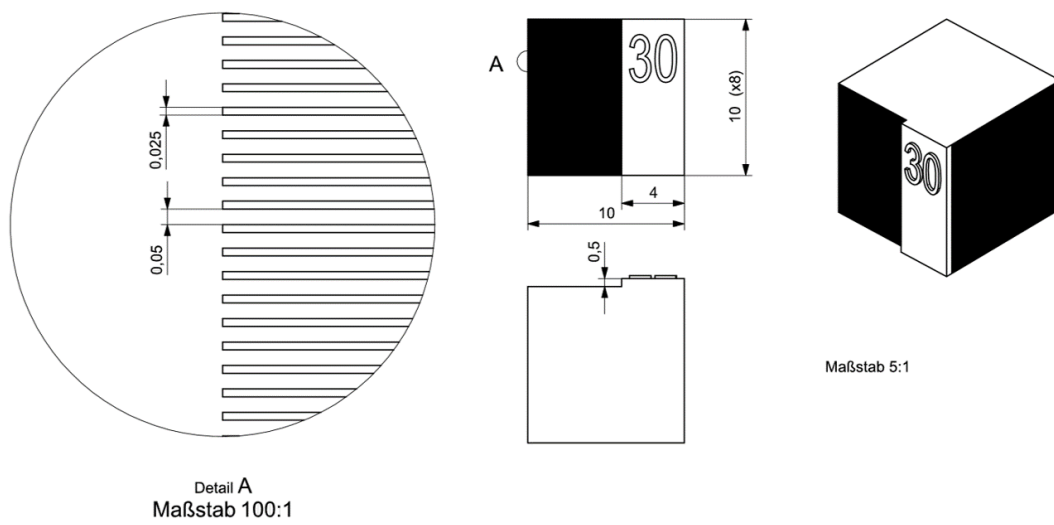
Technische Zeichnung der Dichtewürfel mit einer Schichtdicke von 75 μm
